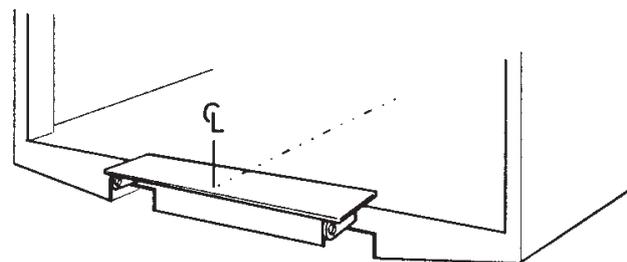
Schrauben oder punktschweißen der Montagevorrichtung an der Hecktraverse
